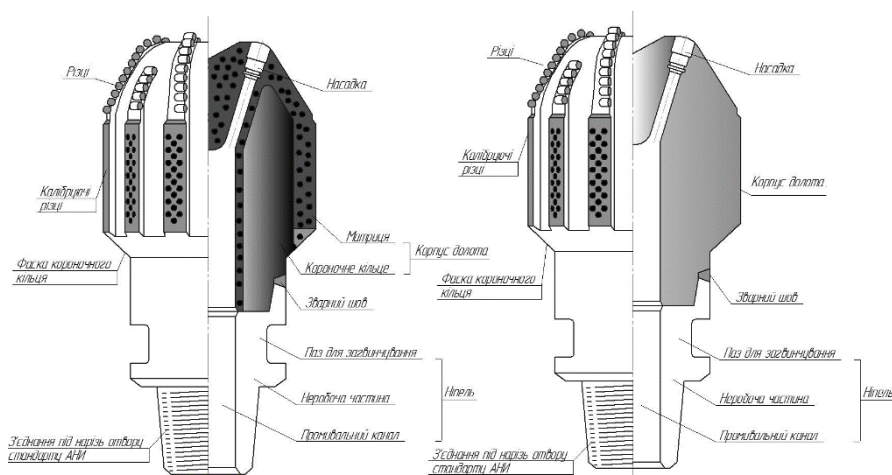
Схеми конструкцій доліт із корпусом із твердого сплаву та сталі
